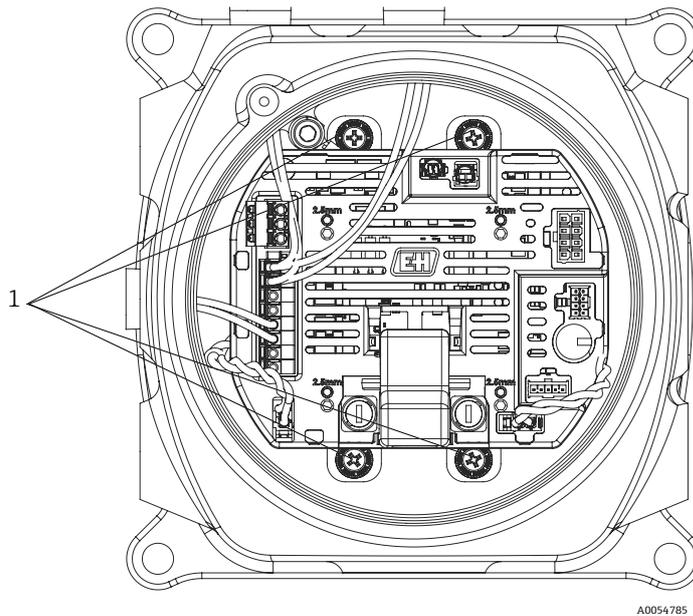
Positionen der unverlierbaren Blechschrauben (1)
